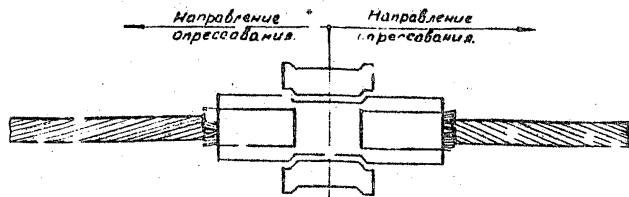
Опрессовка соединительных зажимов типа СВ.
